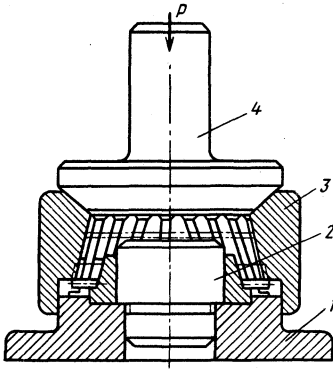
Приспособление для сжатия сепаратора конического роликового подшипника:
